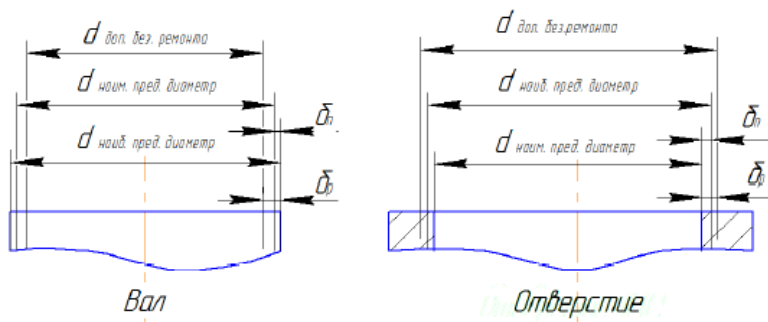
Ремонтные и производственные допуски рабочих поверхностей деталей
